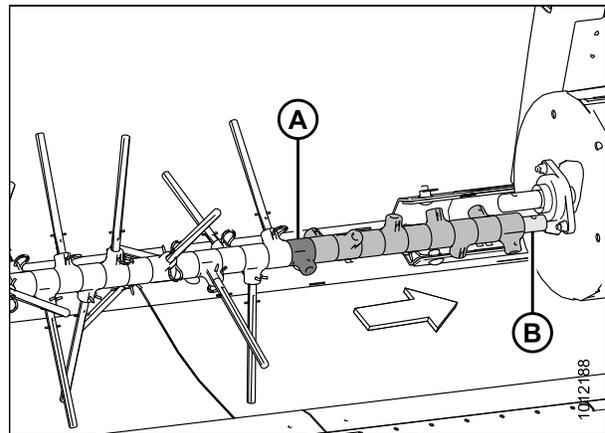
Abrazadera de soporte de dedos de sinfín del lado izquierdo (se muestra la imagen del corte)
